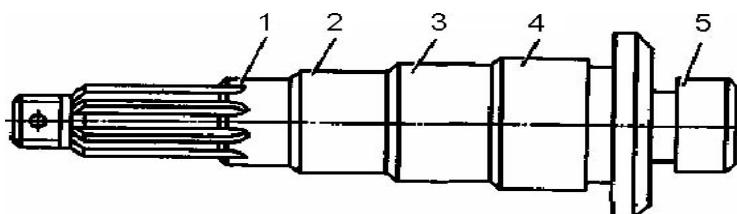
Расположение шеек первичного вала раздаточной коробки:
